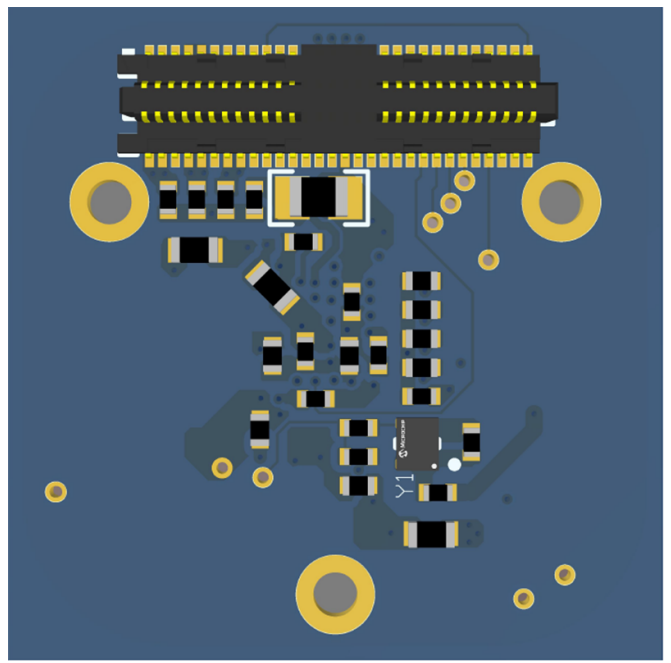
and 図 8 show 3-D PCB views of the assembled boards.
